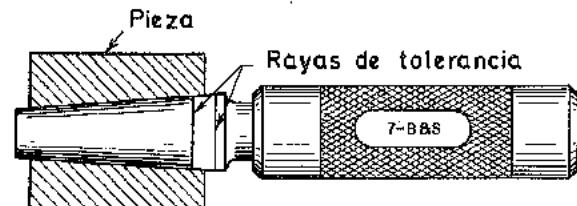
El calibre tapón cónico indica si el diámetro y la conicidad se encuentran dentro de la tolerancia especificada.
